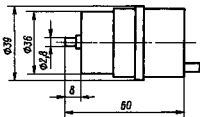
Габаритные и установочные размеры двигателей ДИР-1А, ДИР-1Б
